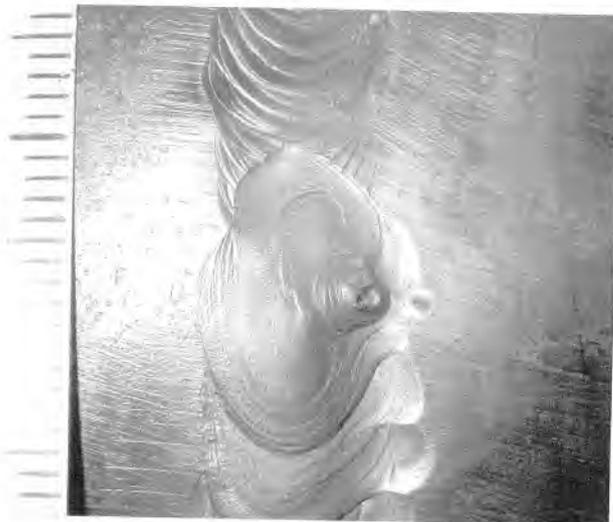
Кратер 1 с небольшим металлическим включением 2 в стыковом сварном соединении строительной конструкции
